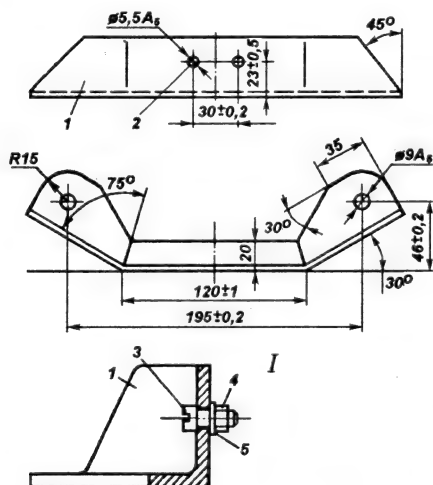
Стопор маховика для облегчения отворачивания гайки
